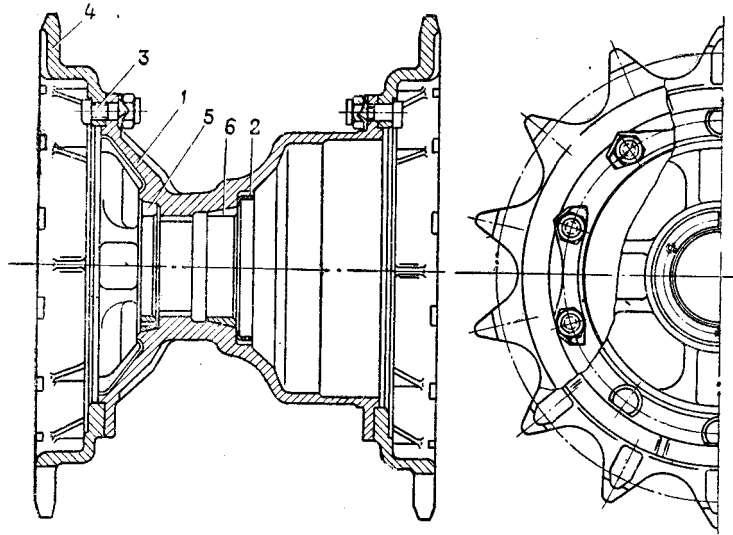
Ведущее колесо для резино-металлической гусеницы:
